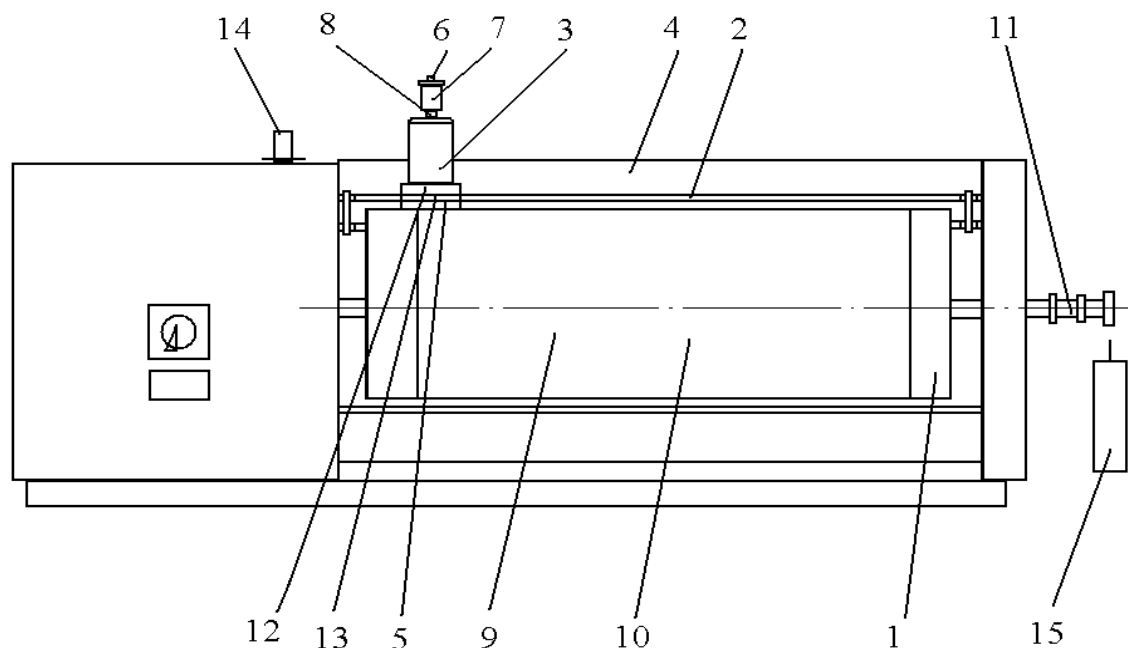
Общий вид истирающей машины: 1 – истирающий валок;
